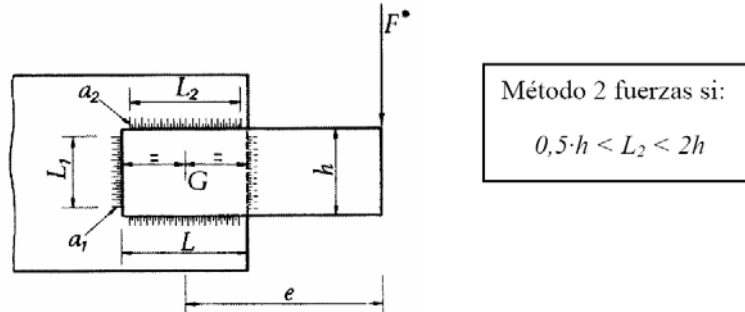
SOLDADURAS FRONTALES Y LATERALES SOMETIDAS A TORSIÓN Y CORTANTE
